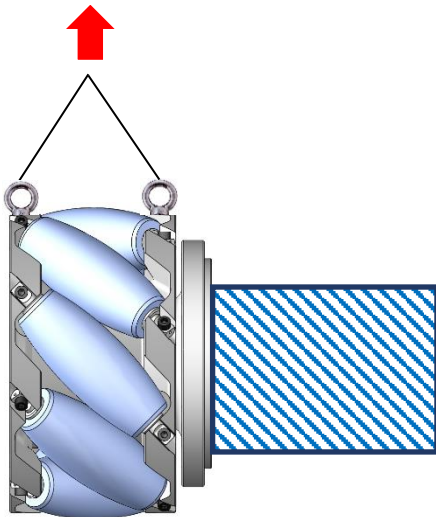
Hebeausrichtung mit installiertem Motor
